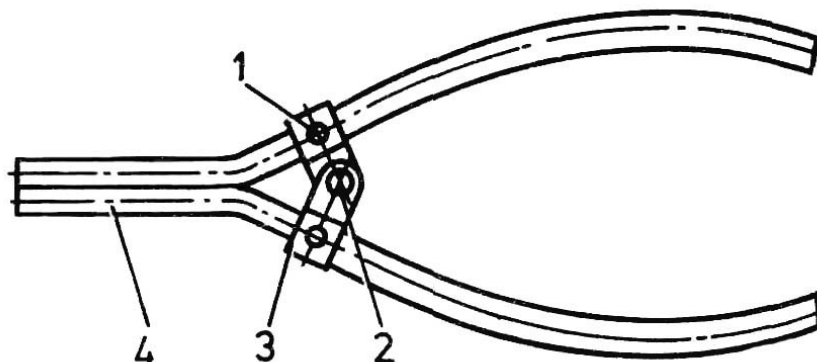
Съемник для снятия стопорного кольца со втулки включения блокировки дифференциала:
